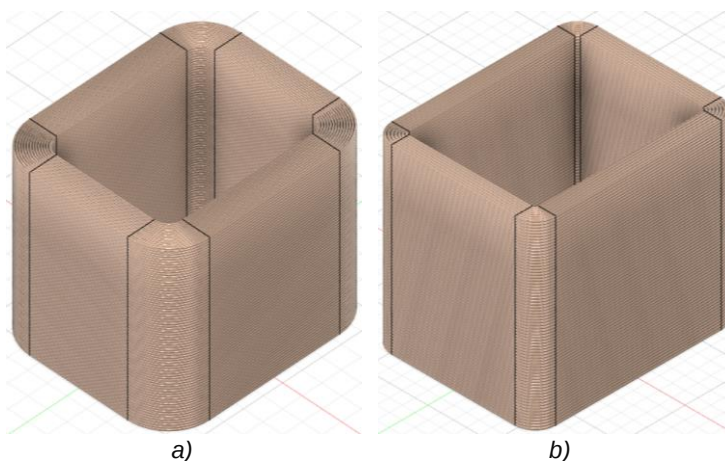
Devanado de a) alta y b) baja tensión - Fuente: El autor
